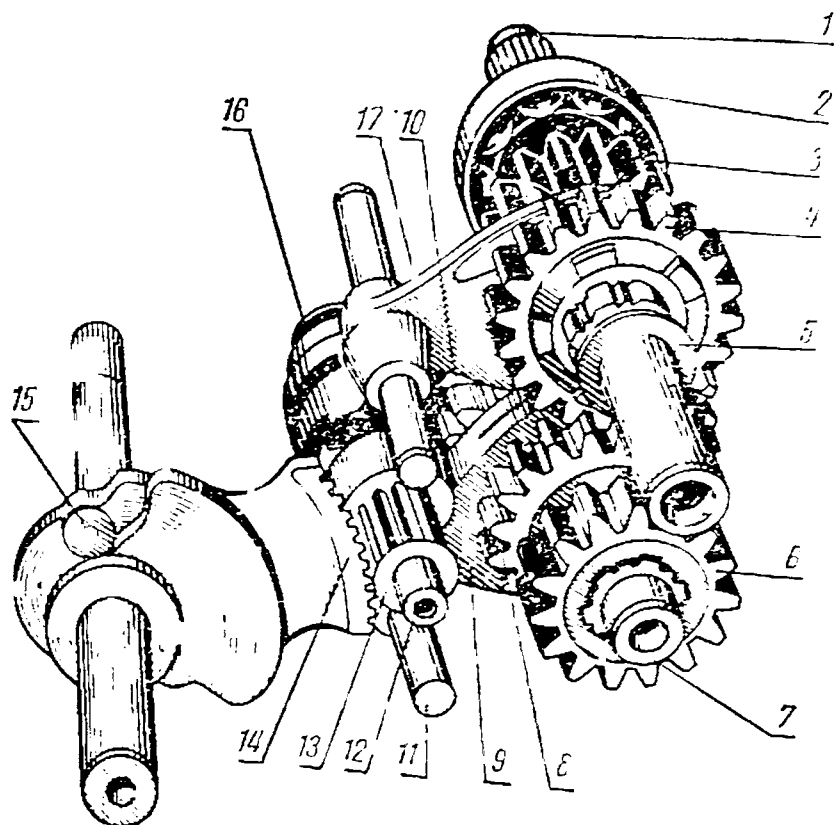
Коробка передач «Иж Планета — Спорт»:
